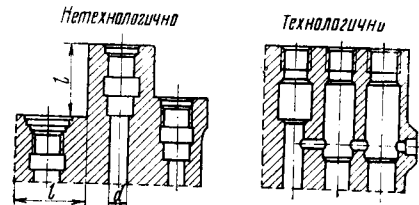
Расположение осей обрабатываемых отверстий.
